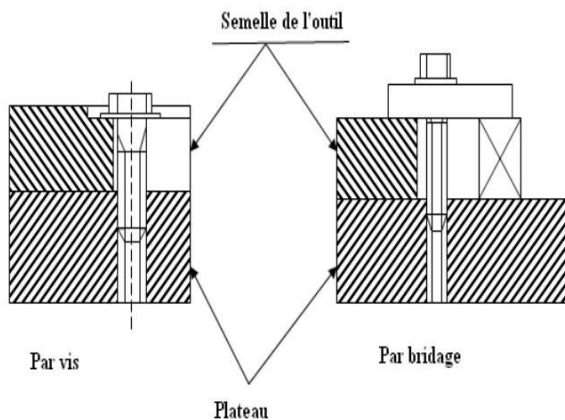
Système de fixation des semelles sur un plateau de presse.
